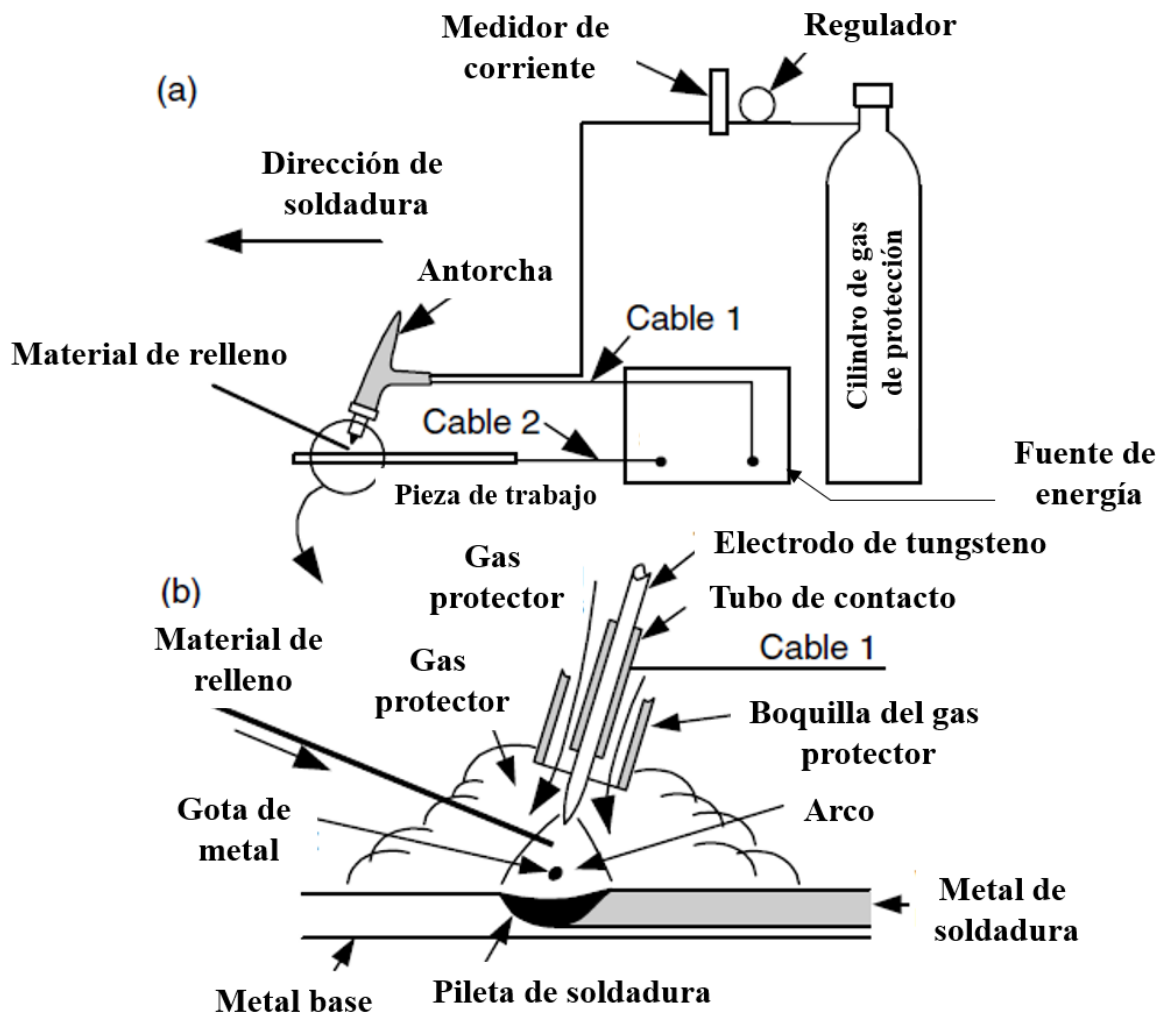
Soldadura por arco de gas-tungsteno: (a) proceso general; (b) área de soldadura ampliada [58].
